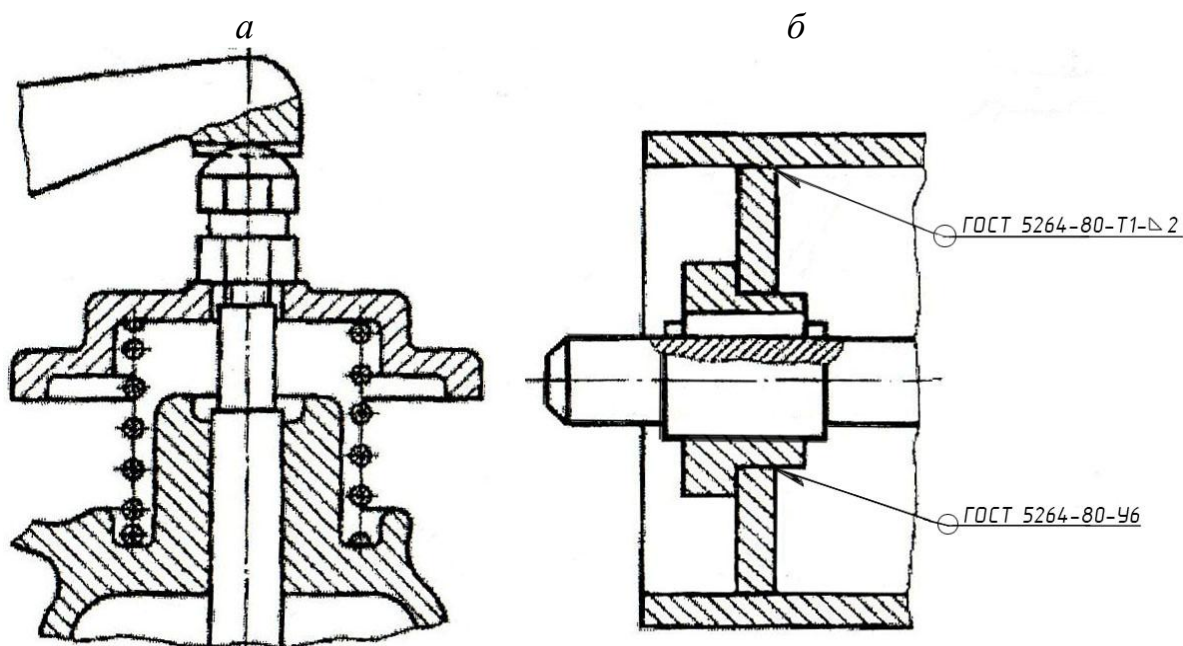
Вычерчивание: *а* – сечений витков пружины; *б* – сечения сварного изделия
